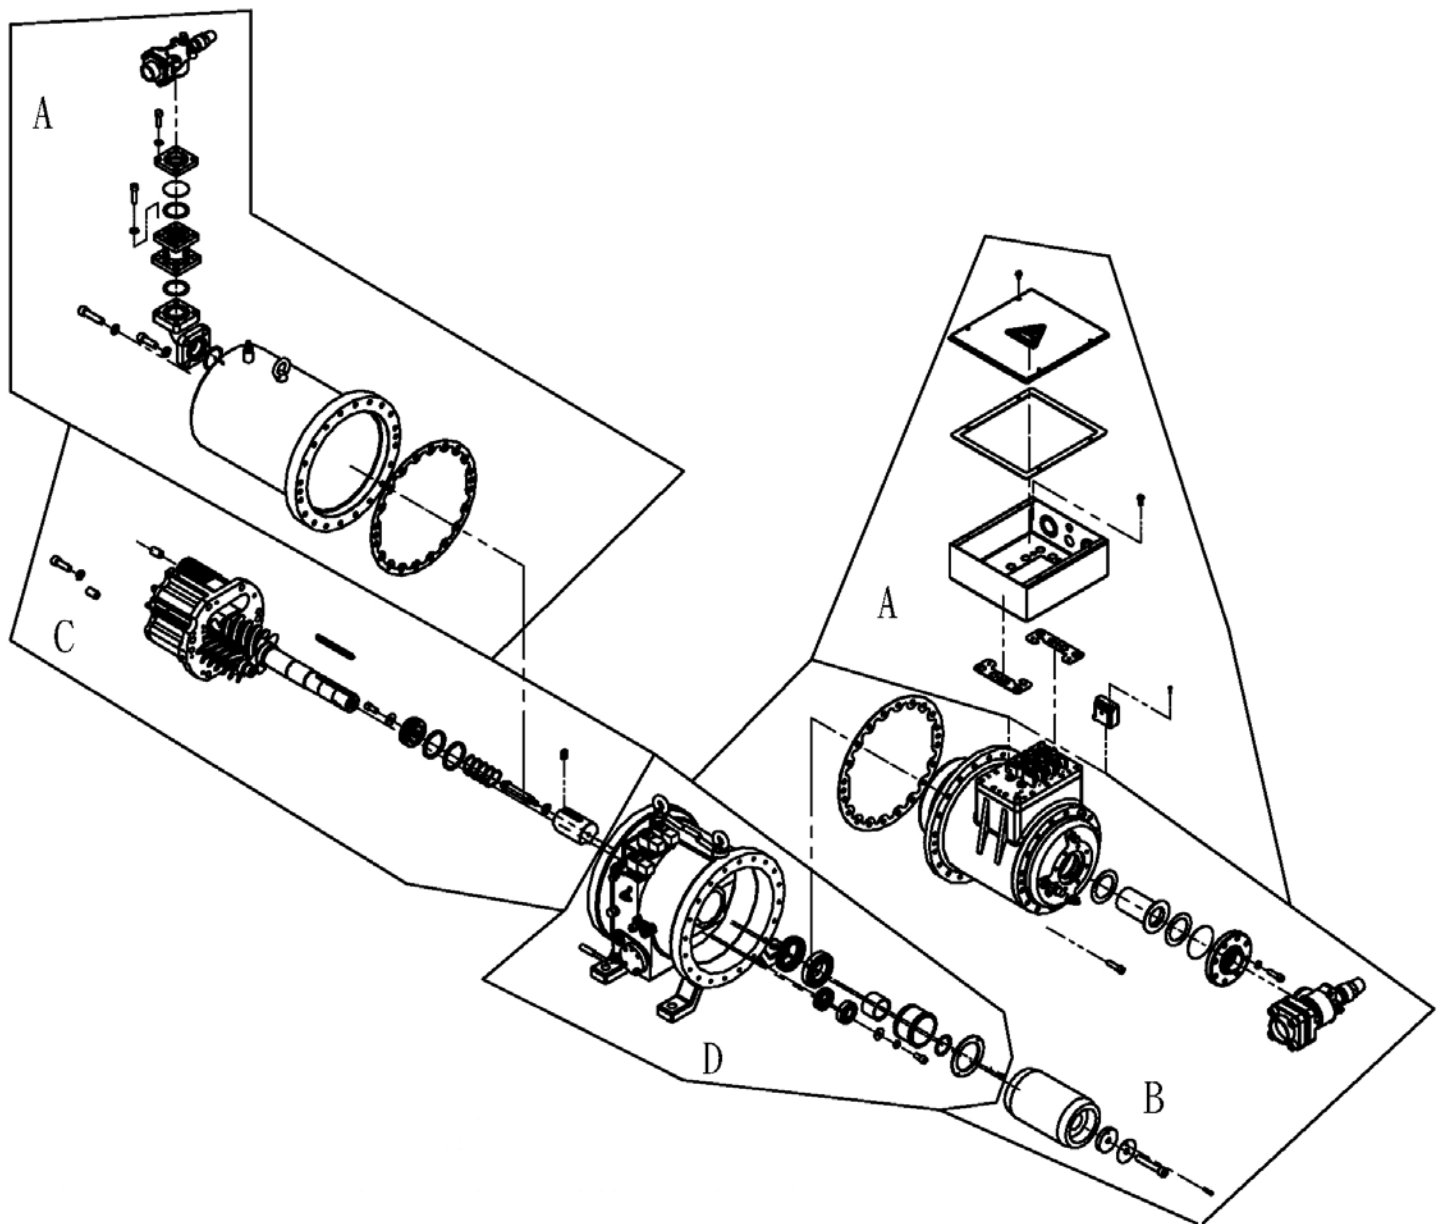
SR-1 (H) ~SR-3 (H) 分解說明/ Disassembly illustration
